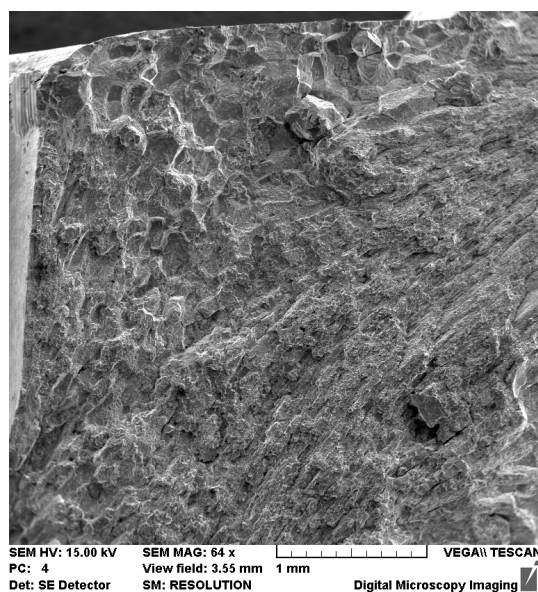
Зоны камневидного (вверху слева) и волокнистого излома на поверхности раскрытой трещины образца К-1
